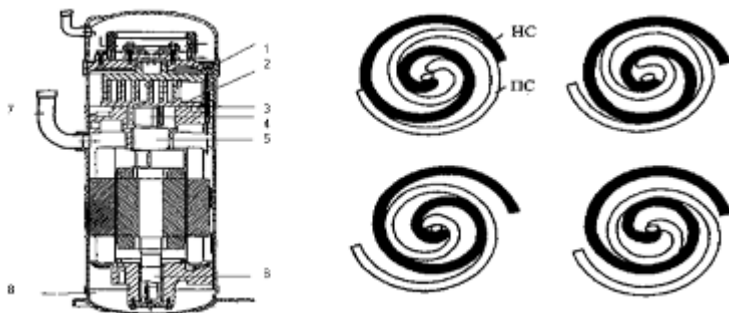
Спиральный компрессор: а - конструкция; б - взаимное положение спиралей по углу поворота
